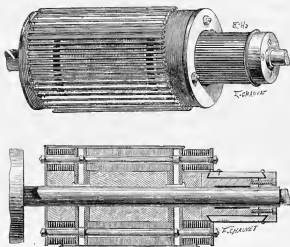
et 149. — Bobine de la machine Edison : perspective et coupe.
